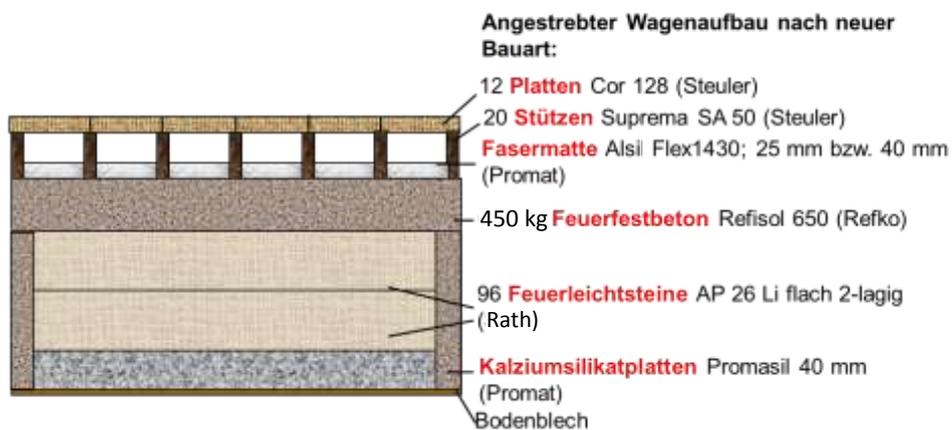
b: Aufbau Ofenwagen, neue Bauweise, mit Faserabdeckung
